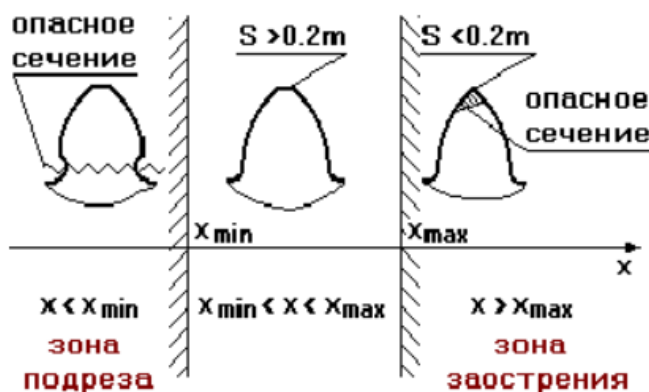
Влияние смещения рейки на профиль зубчатого колеса
